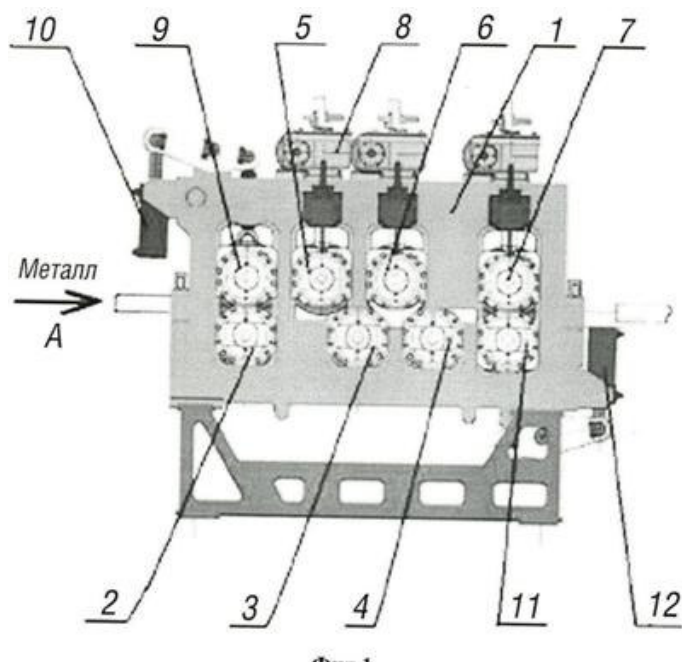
Главный вид машины (по патенту РФ 2459679)
